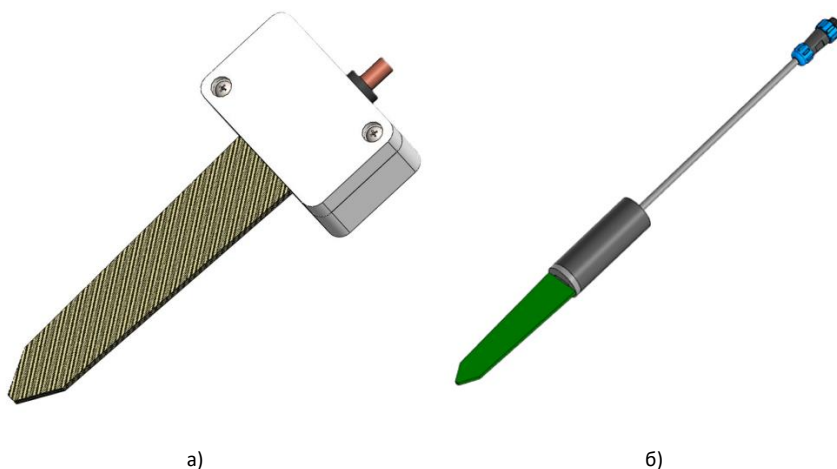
Внешний вид изделия СОКОЛ-ДВП
